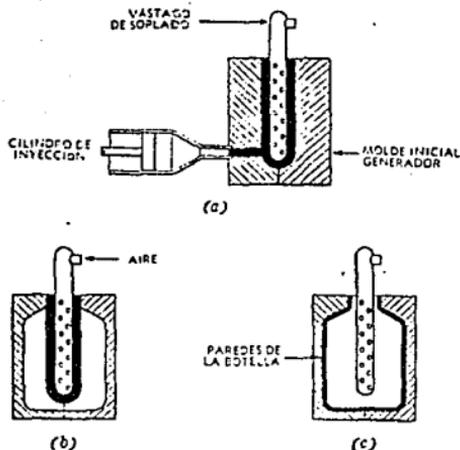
PRINCIPIOS DEL METODO DE INYECCION MOLDEO POR SOPLADO
